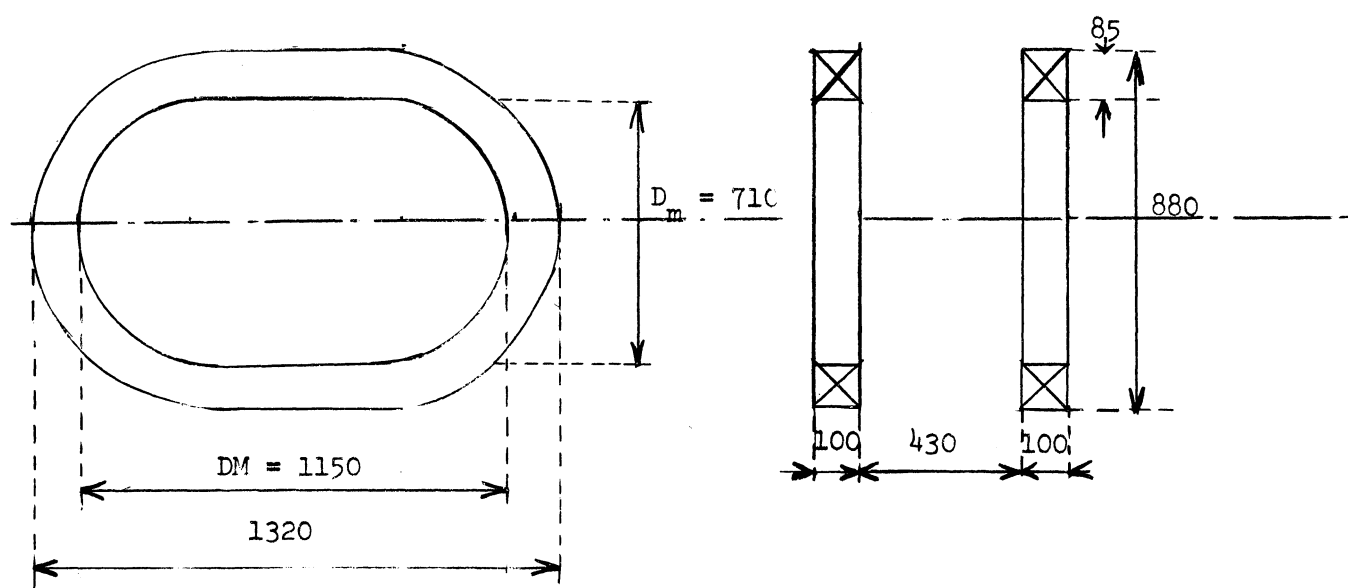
Dimension de la bobine étudiée par la C.G.E.
